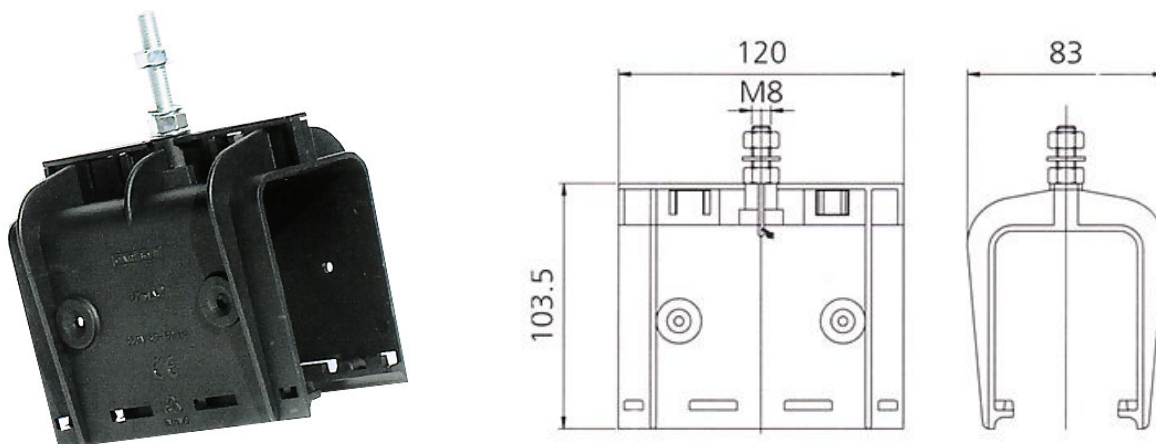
Общий вид соединительной муфты для коробов с точкой фиксации
